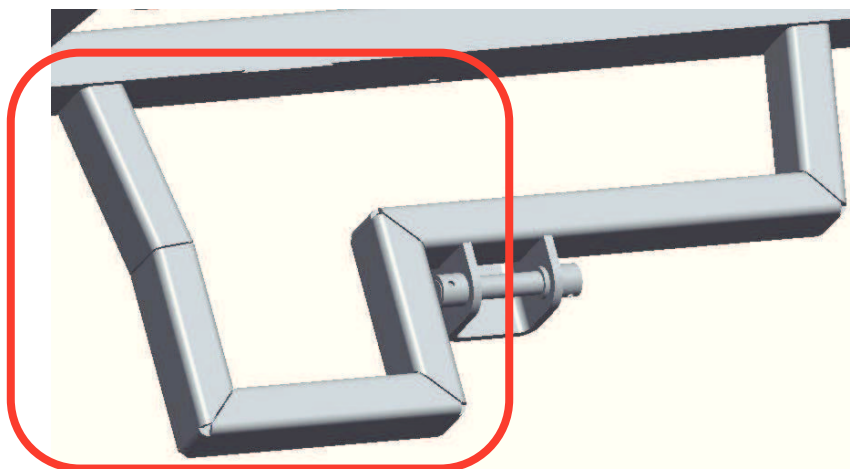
Seřizovací mechanismus motoru č. 1
